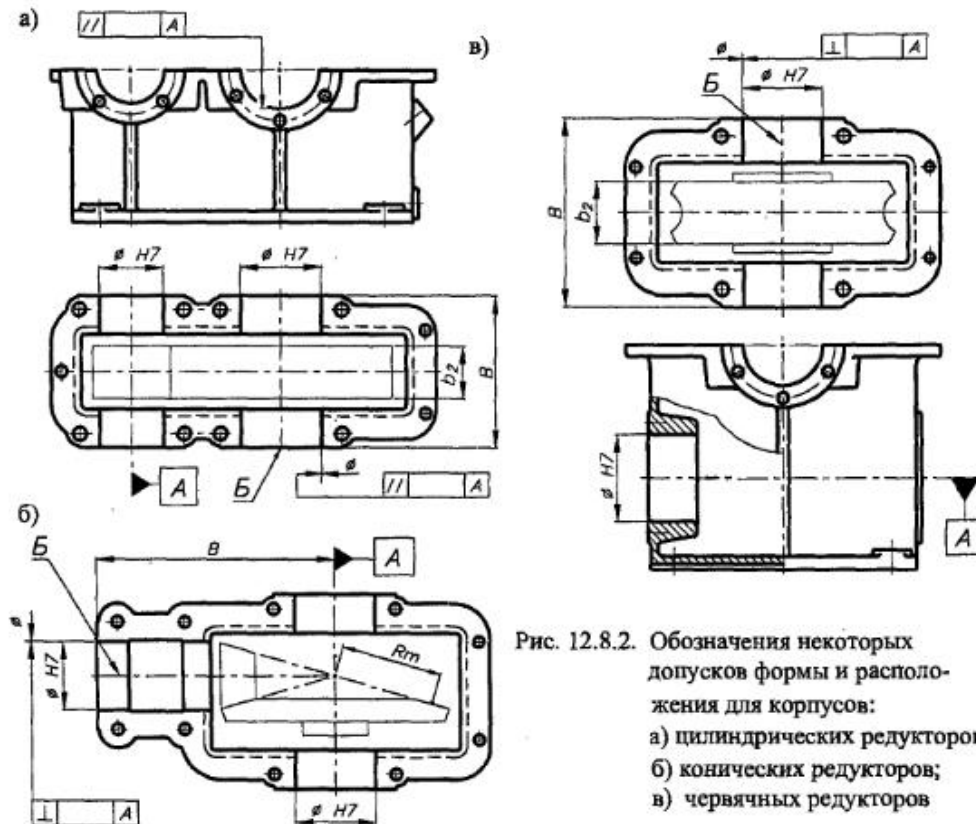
Обозначения некоторых допусков формы и расположения для корпусов: а) цилиндрических редукторов; б) конических редукторов; в) червячных редукторов
